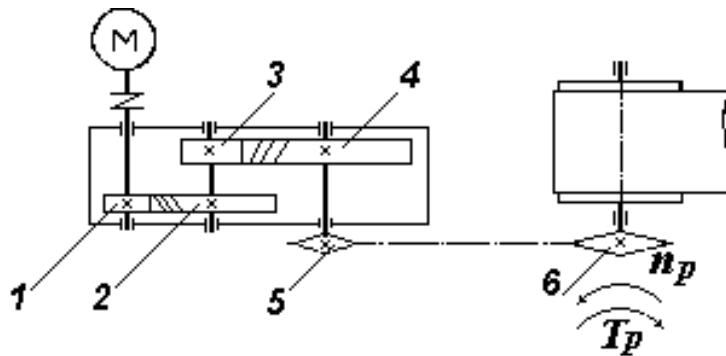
Кинематическая схема привода ленточного конвейера
